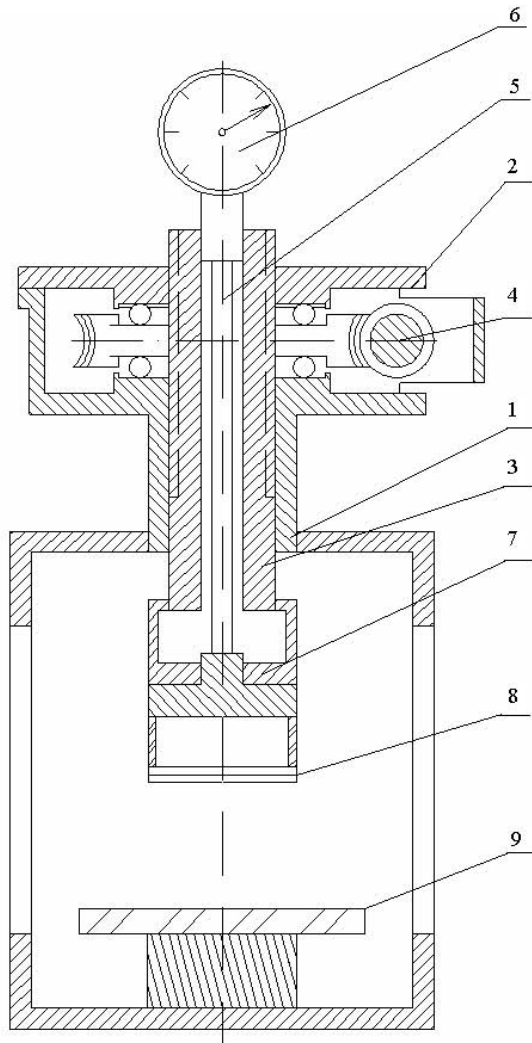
Схема установки для визначення сили різання (патент на корисну модель № 48064 U): 1 – циліндричний корпус; 2 – черв’ячний редуктор; 3 – шток; 4 – черв’ячний вал-шестерня; 5 – штанга динамометра; 6 – динамометр годинникового типу; 7 – трубчаста пружина; 8 – ніж; 9 – предметний стіл.
